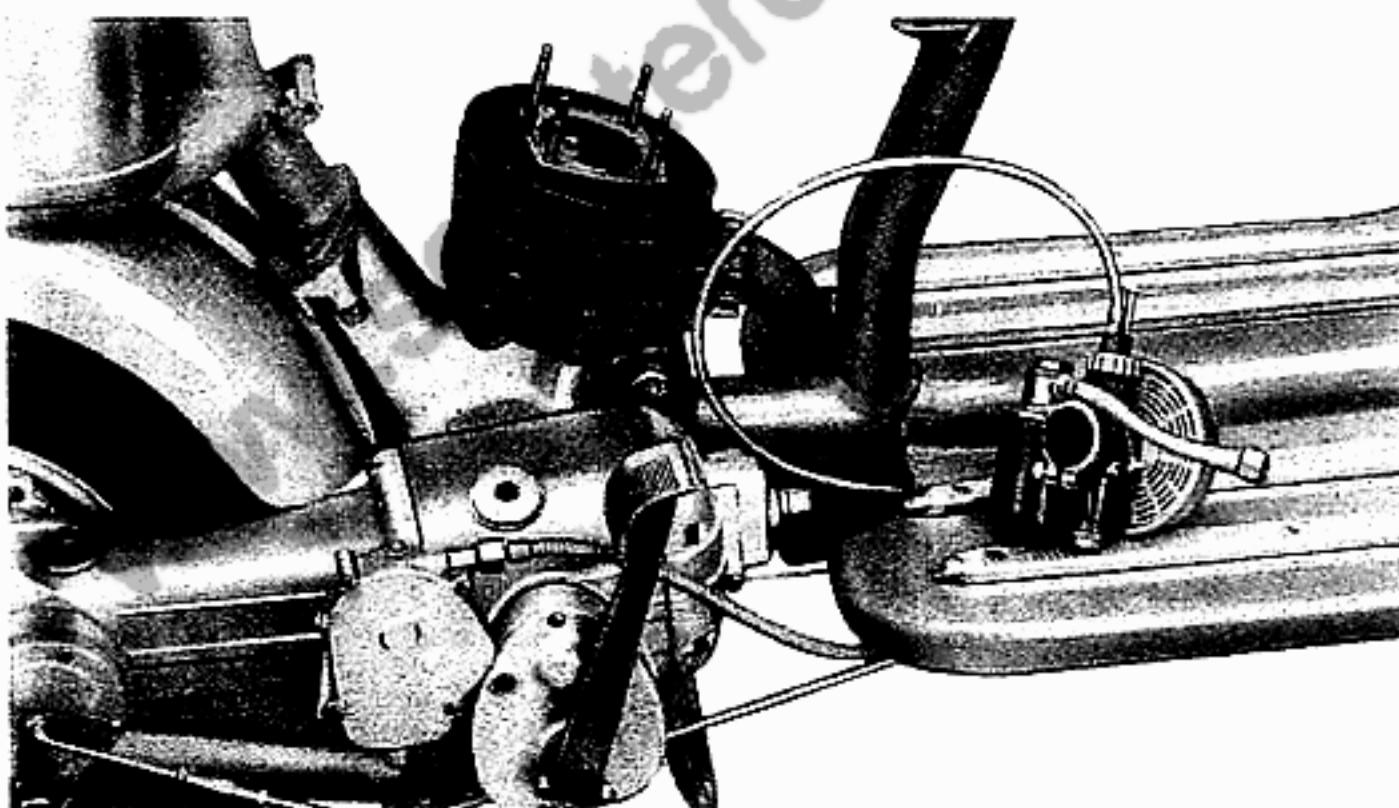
Smontaggio serbatoio, carburatore e testa cilindro.
